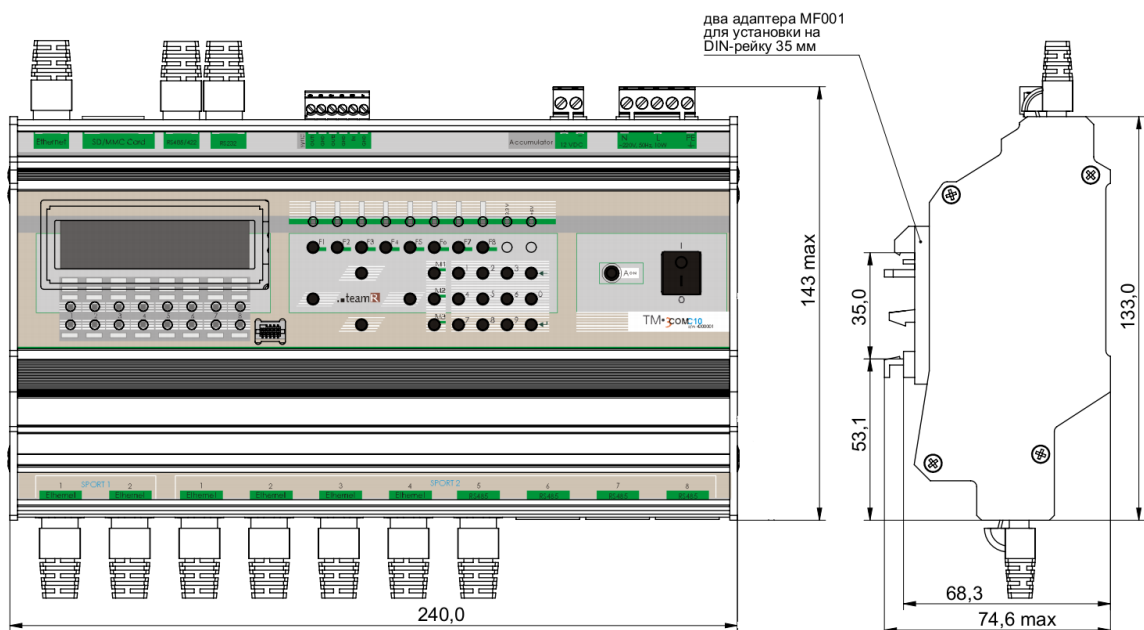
Габаритный чертеж УТМ ПУ «ТМ3com»
